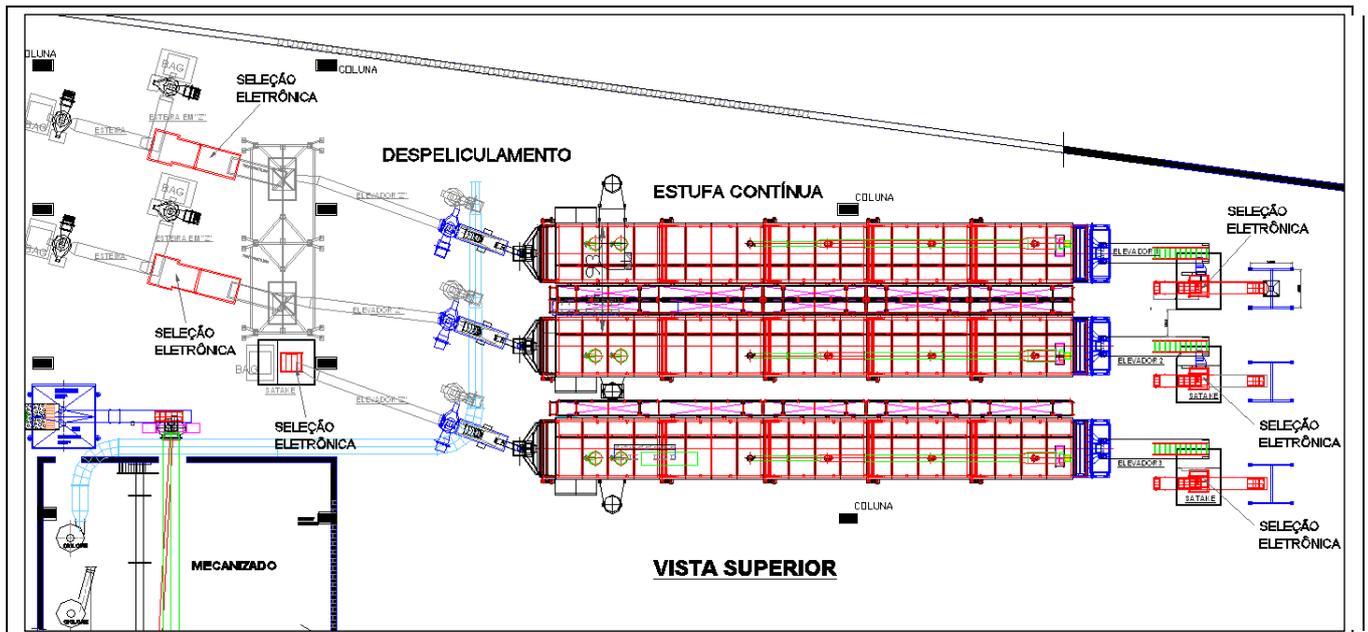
Planta baixa do layout proposta do setor mecanizado e produção da Fábrica 3
